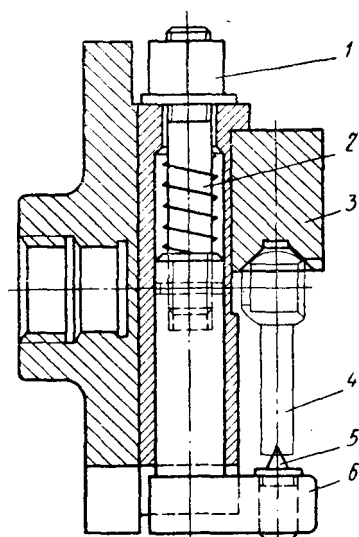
Приспособление для токарной обработки отверстия в деталях технологического ряда ВР-01
